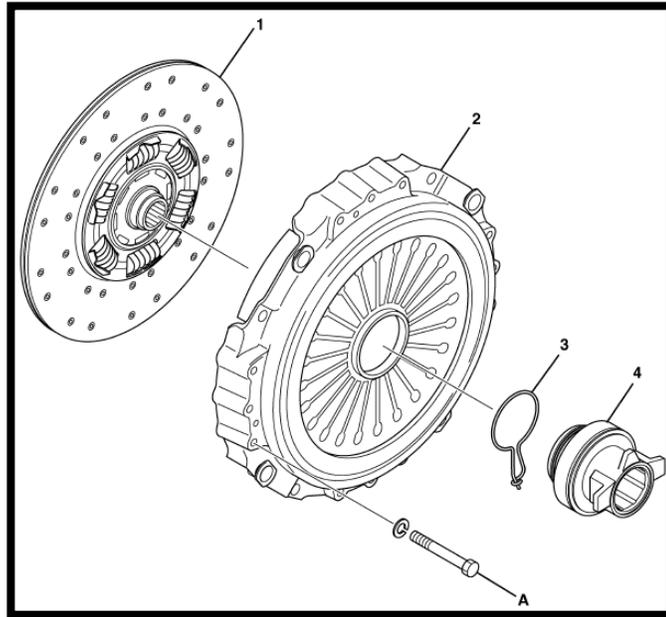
Descripción embrague, volquete: Fuente [32]
